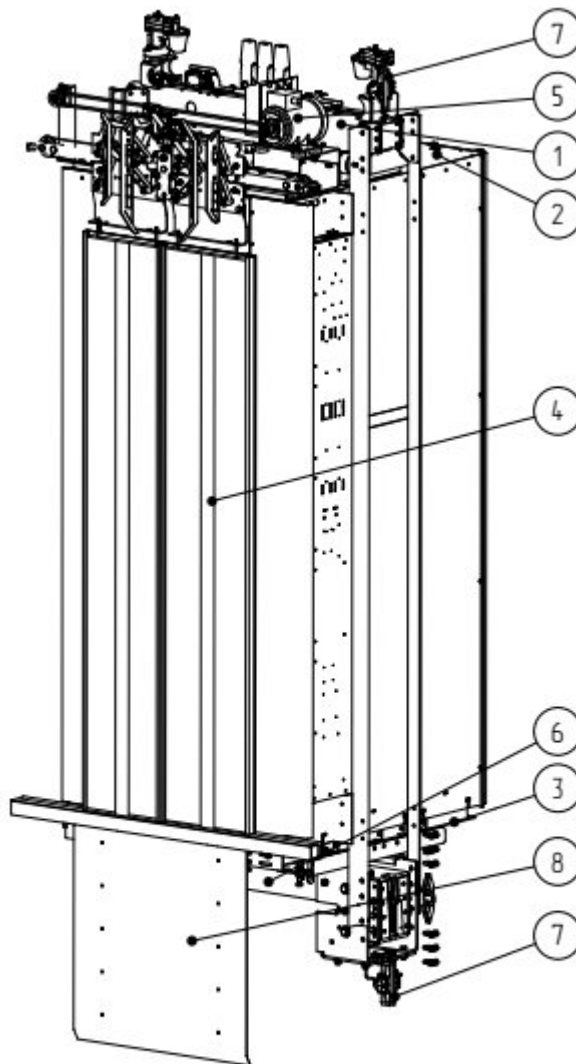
Кабина: 1 – балка верхняя; 2 – потолок; 3 – пол; 4 – створки; 5 – привод дверей кабины; 6 – балка нижняя; 7 – башмак скользящий; 8 – фартук.
